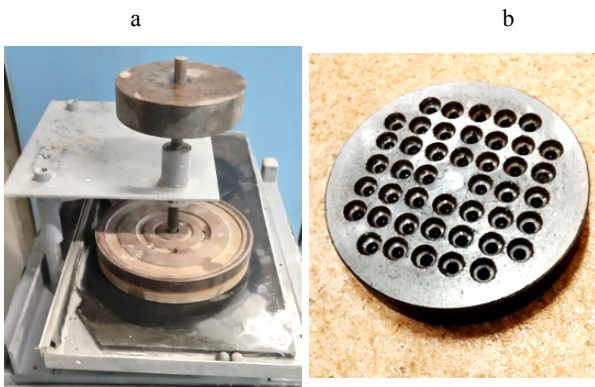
а – устройство для шлифования шариков; б – шлифовальный диск с коническими отверстиями
